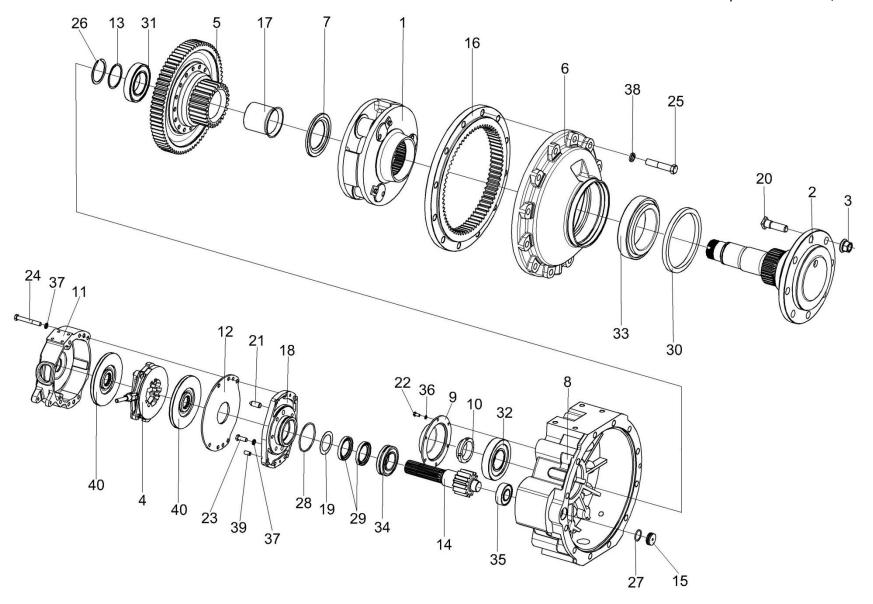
Редуктор бортовой КЗК-10-0107200-04 (лист 2)
